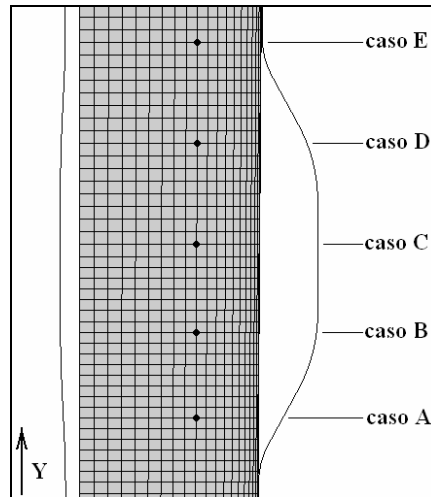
Posição do cordão de soldadura para os diferentes casos de estudo.
